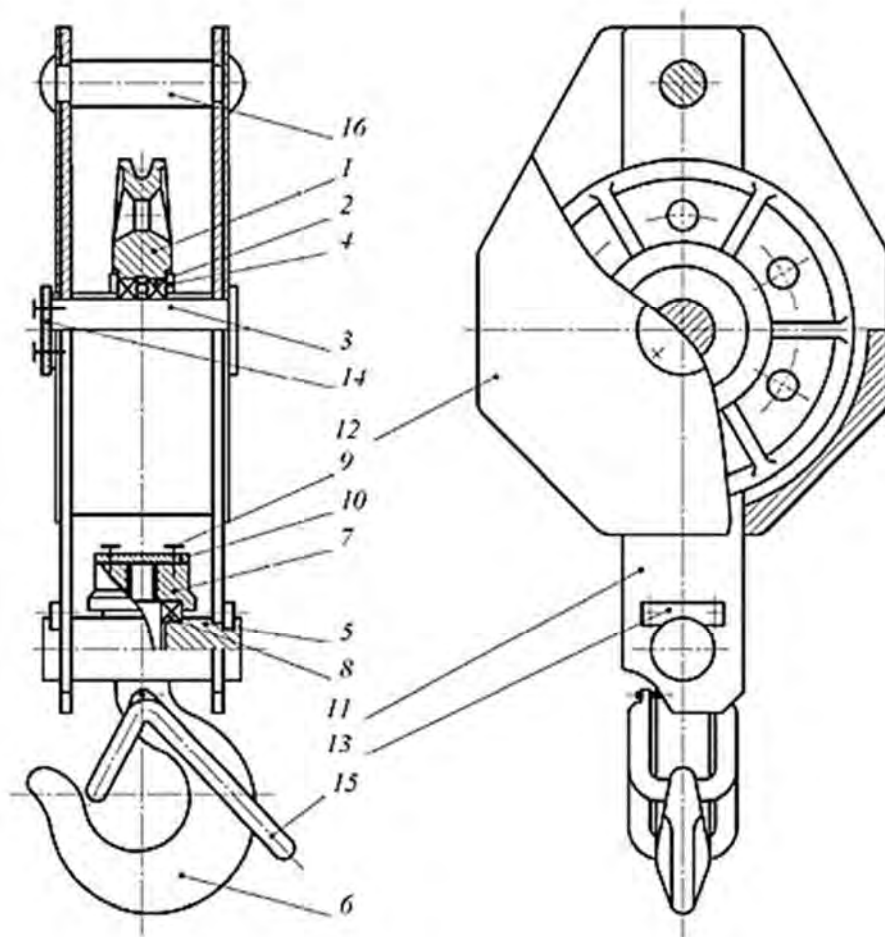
Нормальная крюковая подвеска: 1 – блок; 2 – радиальный подшипник; 3 – ось блока; 4 – крышка подшипника; 5 – траверса; 6 – крюк; 7 – гайка; 8 – упорный подшипник; 9 – винт; 10 – торцевая шайба; 11 – серьга; 12 – защитный лист; 13 – стопорная планка; 14 – стопорная шайба; 15 – замок; 16 – ось крепления свободного конца каната
